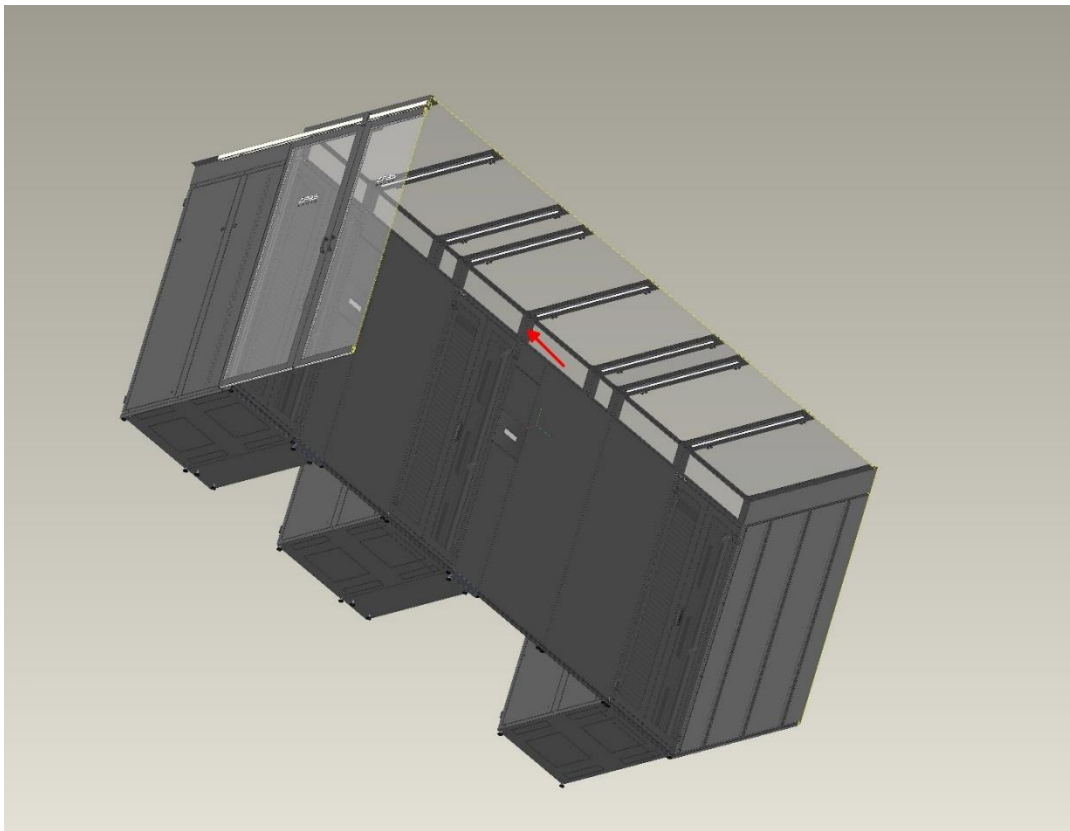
Podłączenie kabla zasilającego podstawowego w panelu zasilającym.
